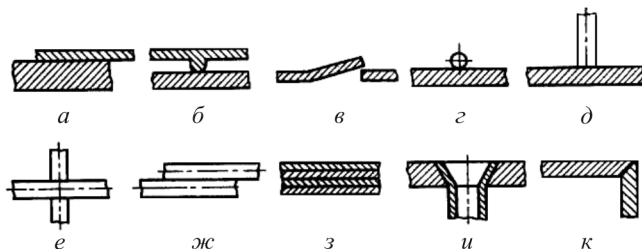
Основные типы сварных соединений металлов: *a* – внахлестку; *б* – по рельефам; *в* – с раздавливанием кромок; *г* – параллельное круглого элемента с плоским; *д* – встык круглого элемента с плоским; *е* – крестообразное круглых элементов; *ж* – параллельное круглых элементов; *з* – многослойных деталей и пленок; *и*, *к* – угловое
